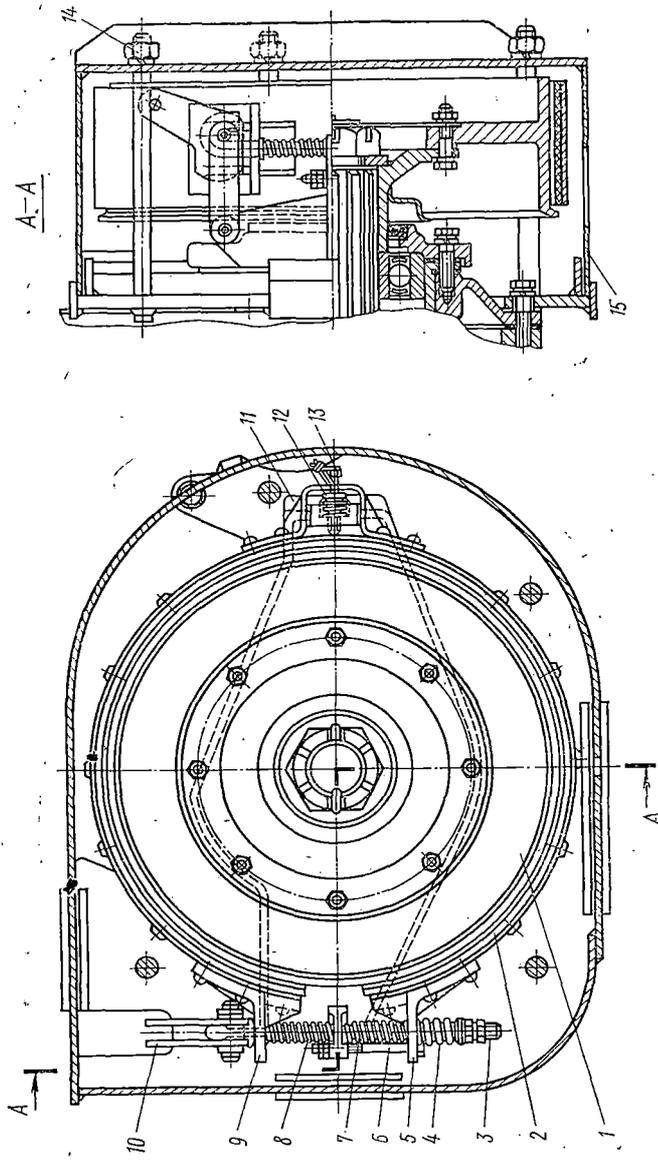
Ручной тормоз самоходного скрепера ДЗ-11М:
